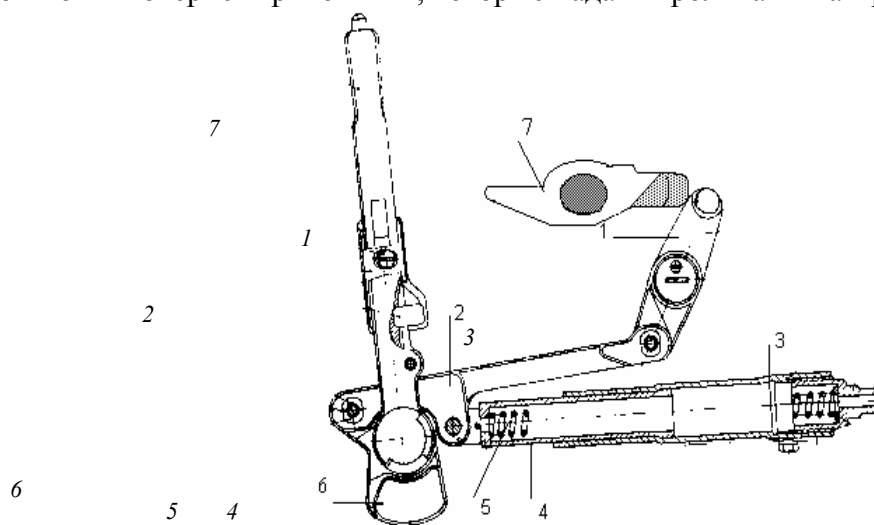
Открывающий и закрывающий механизмы полуавтоматики затвора
